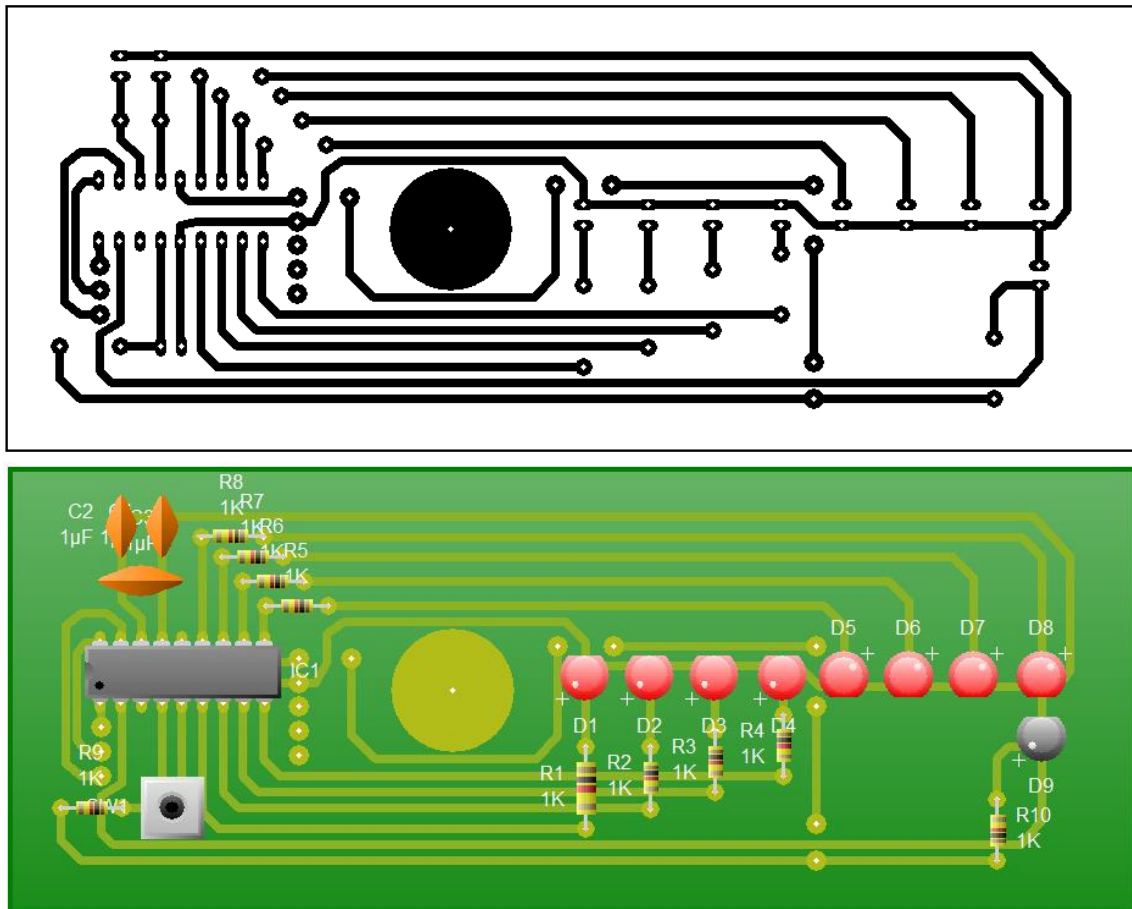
Diseño placa circuito Propeller Clock, arriba vista de la placa fresada y abajo vista real de la placa.
